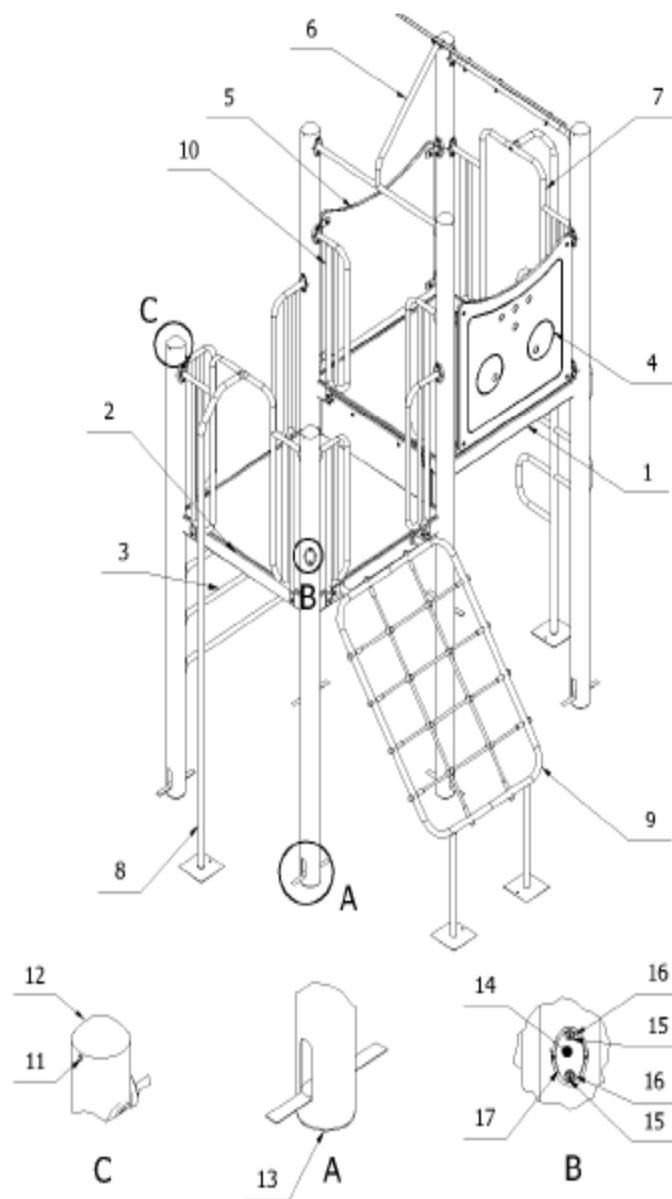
Przykładowe rozmieszczenie fundamentów betonowych pod urządzenie sprawnościowo – wspinaczkowe.
